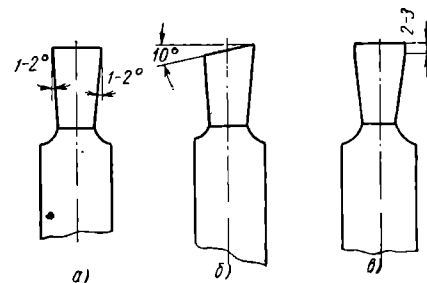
Проходной резец конструкции В. К. Семинского.
